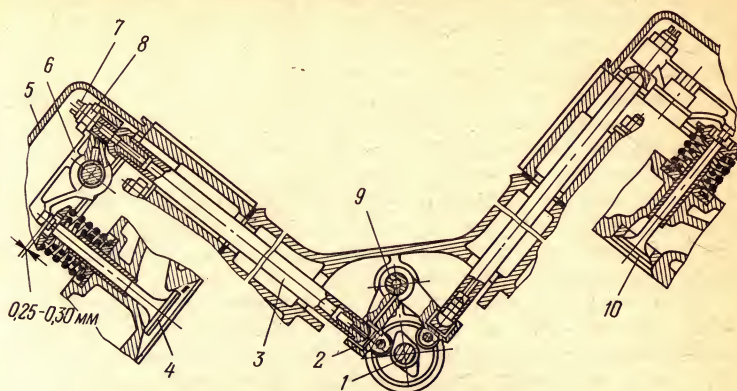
Схема регулировки зазоров клапанов двигателя ЯМЗ-240Б: 1 — распределительный вал; 2 — толкатель; 3 — штанга толкателя; 4 — впускной клапан; 5 — крышка головки цилиндров; 6 — коромысло; 7 — регулировочный винт; 8 — контргайка; 9 — ось толкателей; 10 — выпускной клапан
